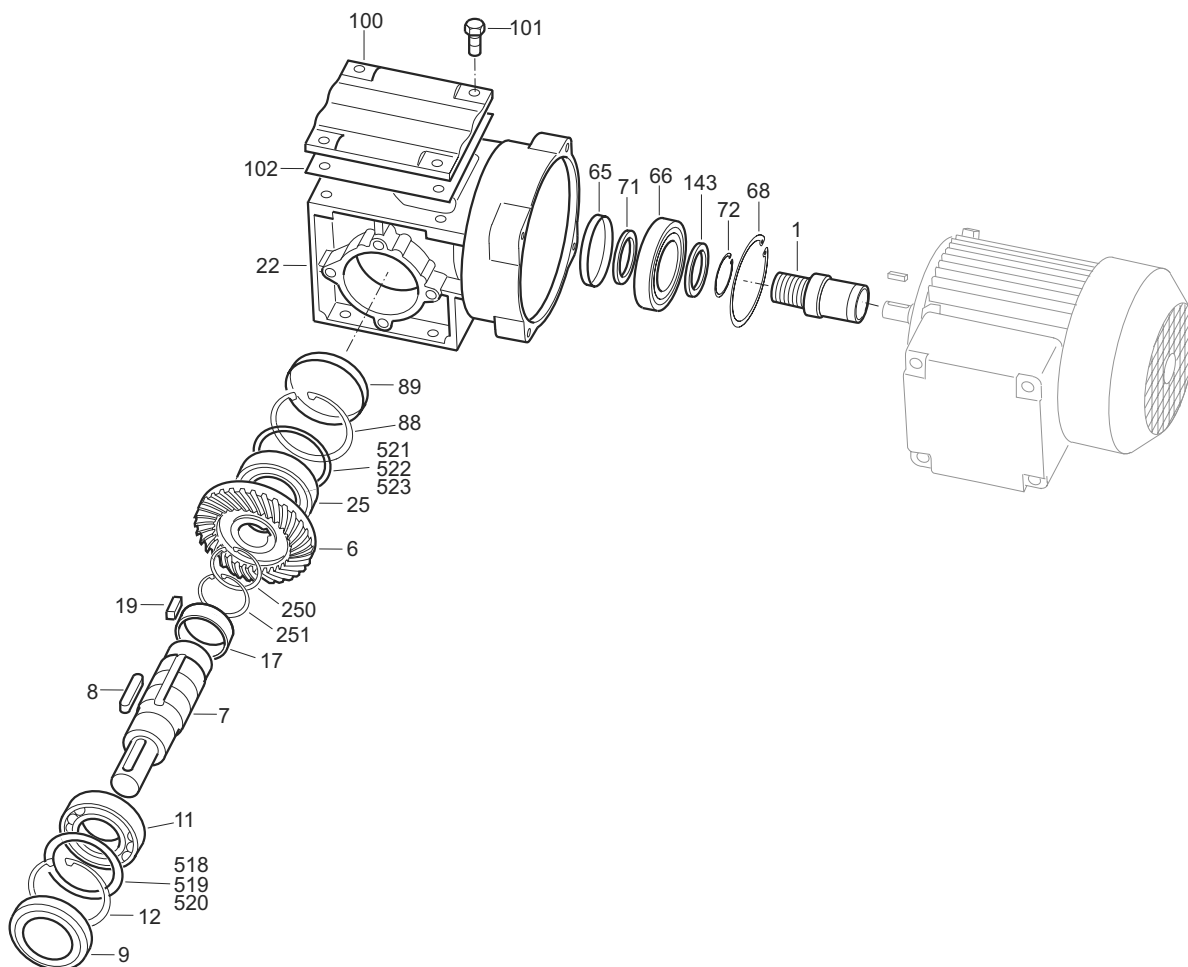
Prinzipieller Aufbau SPIROPLAN®-Getriebe
